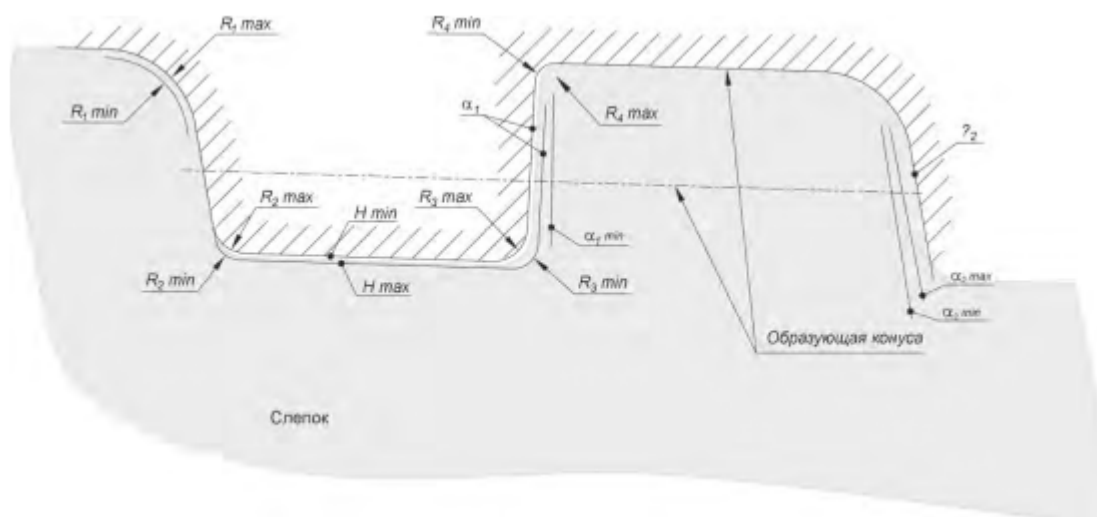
Контроль профиля резьбы муфты по слепкам
